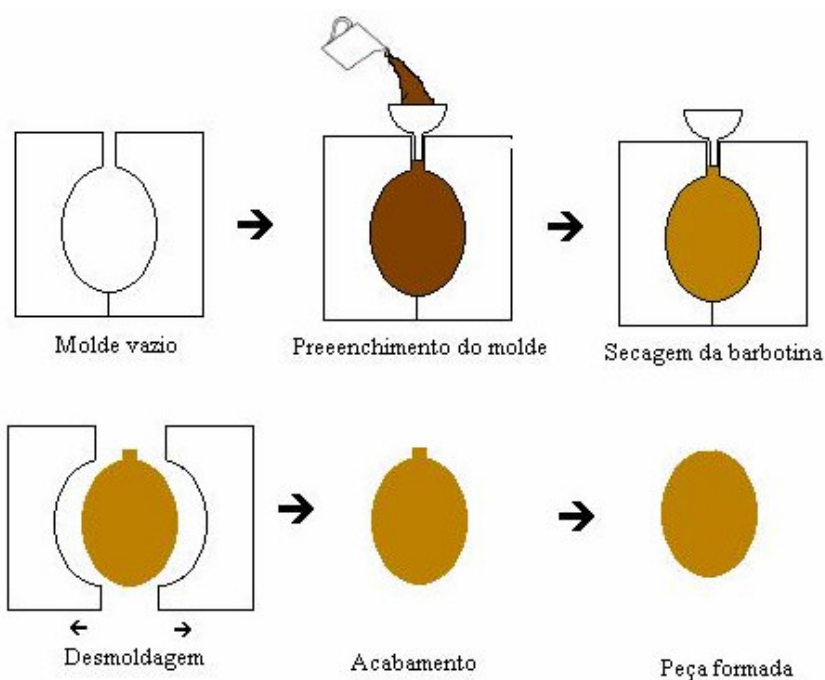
Ilustração da etapa de moldagem do processo de colagem
